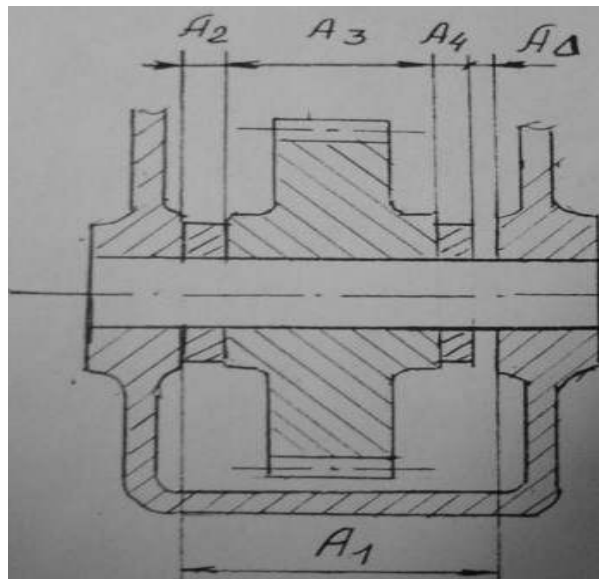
Зубчатое колесо и распорные кольца в редукторе
